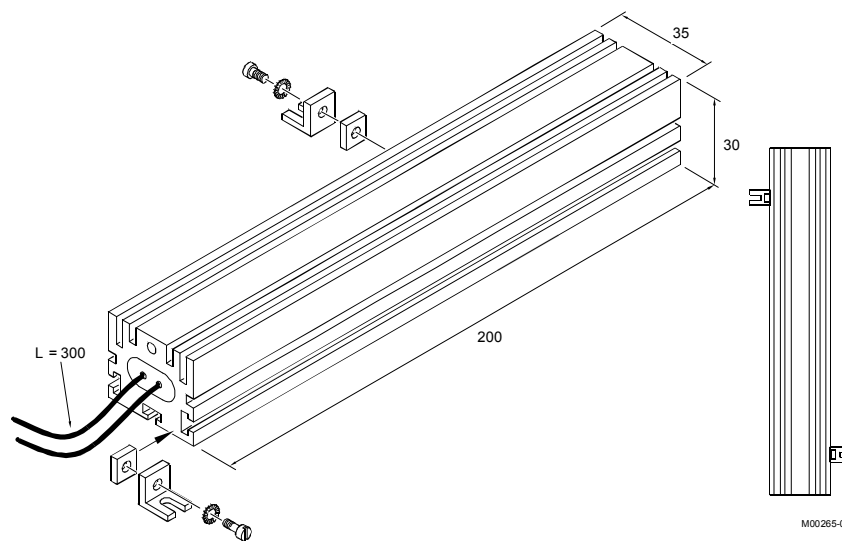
Габаритные размеры резистора 56-100 Ом/350 Вт
